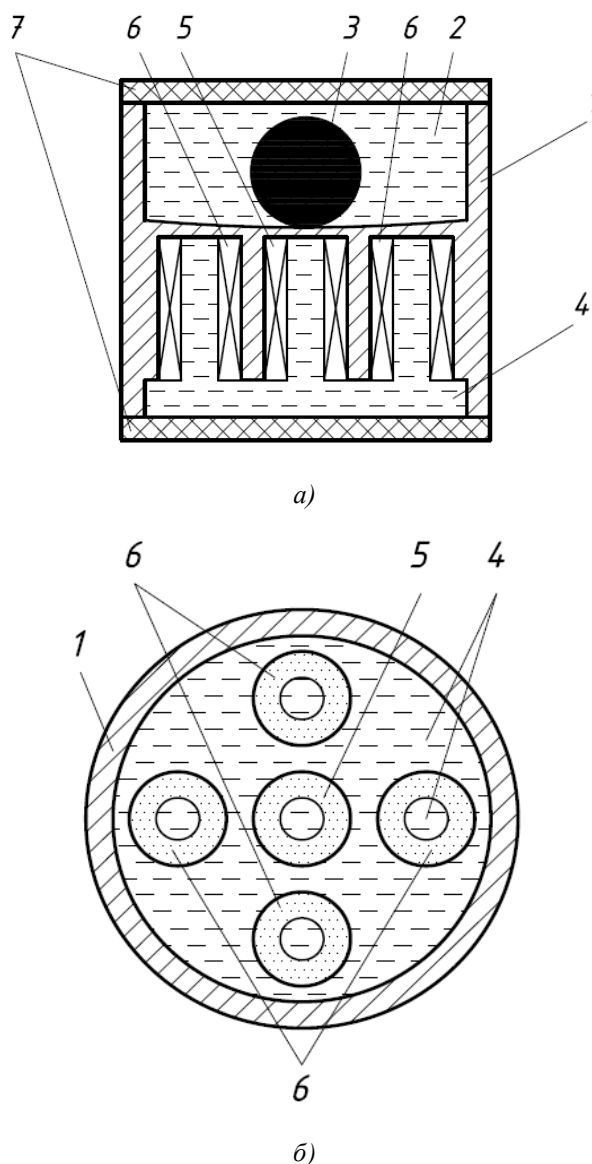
Двухосный первичный преобразователь угла наклона: 1 – корпус; 2 – магнитная жидкость; 3 – немагнитный шарик; 4 – магнитная жидкость; 5 – первичная обмотка; 6 – вторичные обмотки; 7 – крышка; а – в разрезе; б – вид снизу. / Shows the primary biaxial converter of the inclinometer tilt angle: 1 – case; 2 – magnetic fluid; 3 – non-magnetic ball; 4 – magnetic fluid; 5 – primary winding; 6 – secondary winding; 7 – lid; а – in section; б – bottom view.
